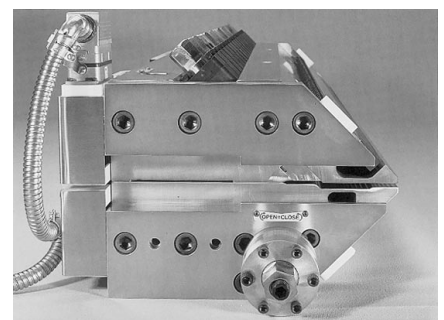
Seitenansicht eines „Uni-Flex“ Werkzeugs mit abgenommener Seitendichtung
